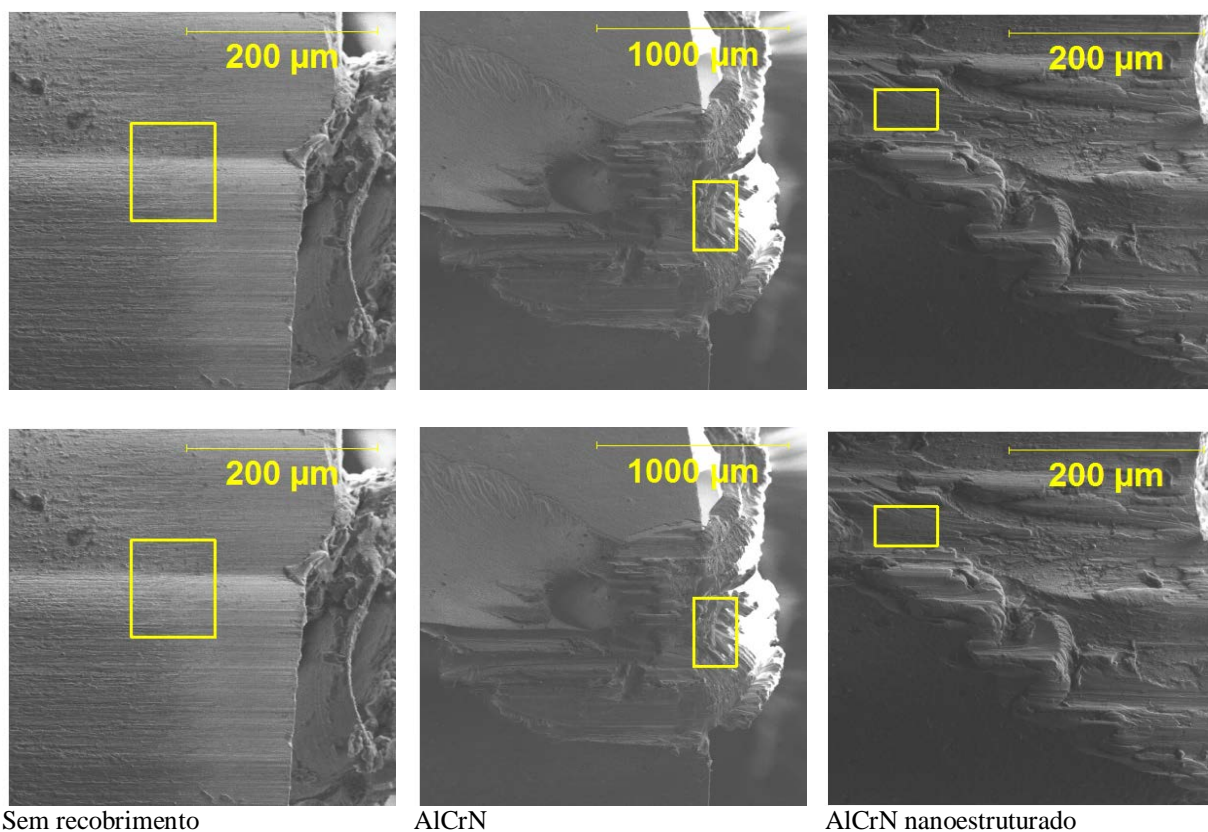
Micrografias utilizando MEV demonstrando a superfície de folga das ferramentas de corte juntamente com suas EDS no torneamento com velocidade de corte de 250 m/min, avanço de 0,20 mm/rev e profundidade de usinagem de 0,75 mm.
